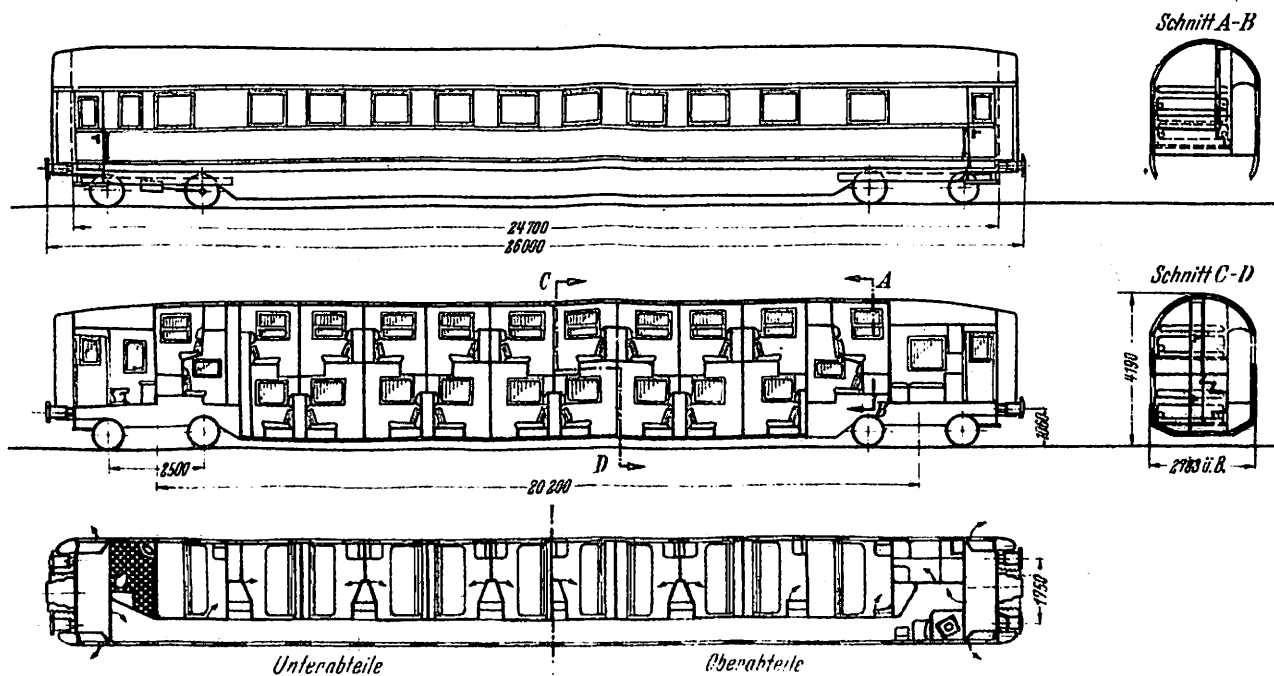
Doppelstöckiger Einbettabteil-Schlafwagen (Linke-Hofmann, Breslau).
